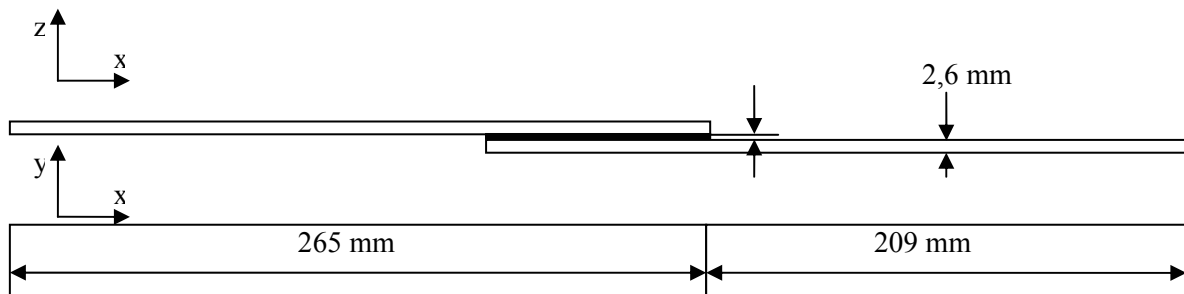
Géométrie des éprouvettes de simple recouvrement
